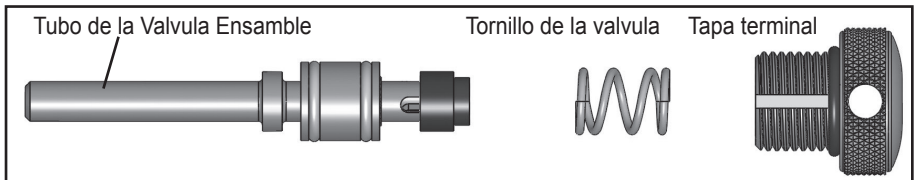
Ensamble de la Valvula, Tornillo de la valvula, y Tapa terminal
